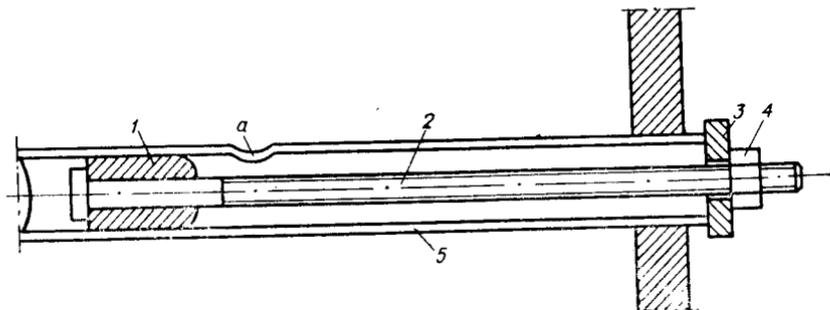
Приспособление для правки вмятин в трубах:
